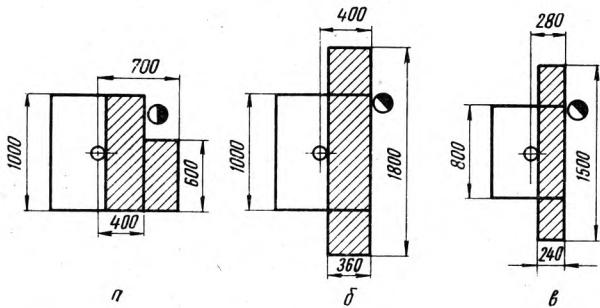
Рабочие зоны станков, оснащенных дополнительными навесными столами (а — по ширине станка; б, в — по длине станка)
